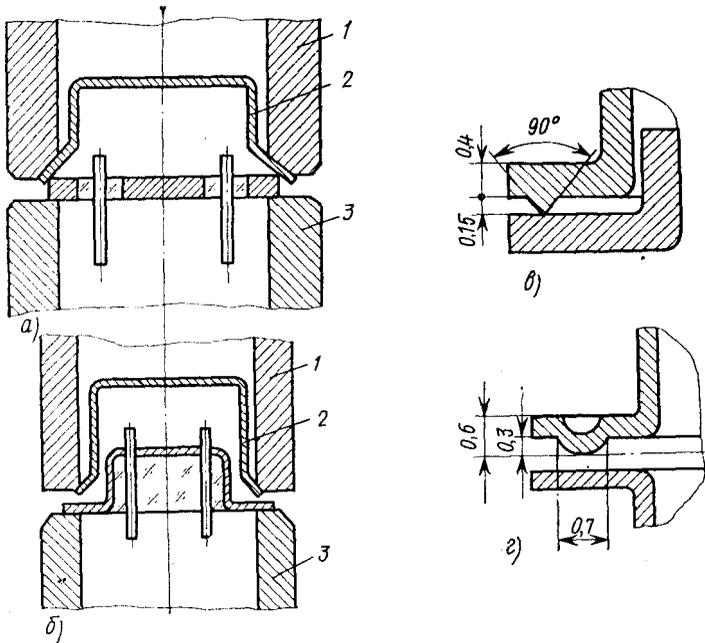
Приемы герметизации корпусов приборов контактной конденсаторной сваркой
